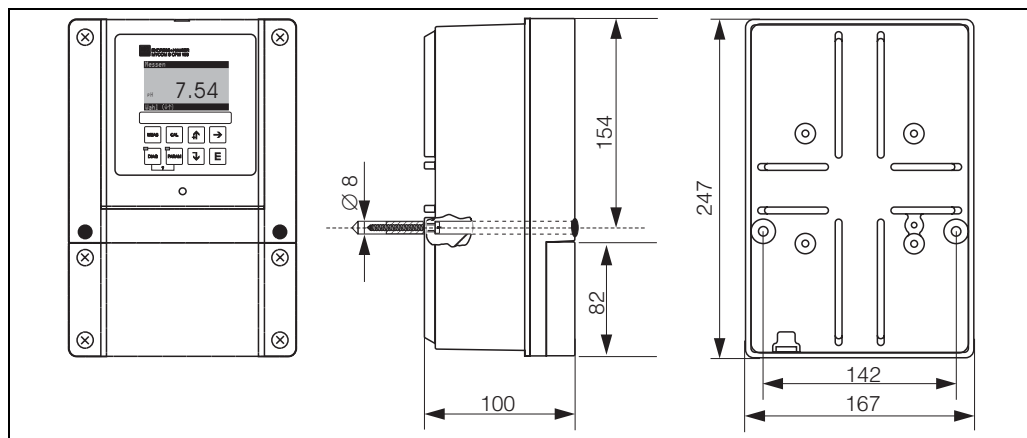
Dimensions du transmetteur de mesure CLM153.
